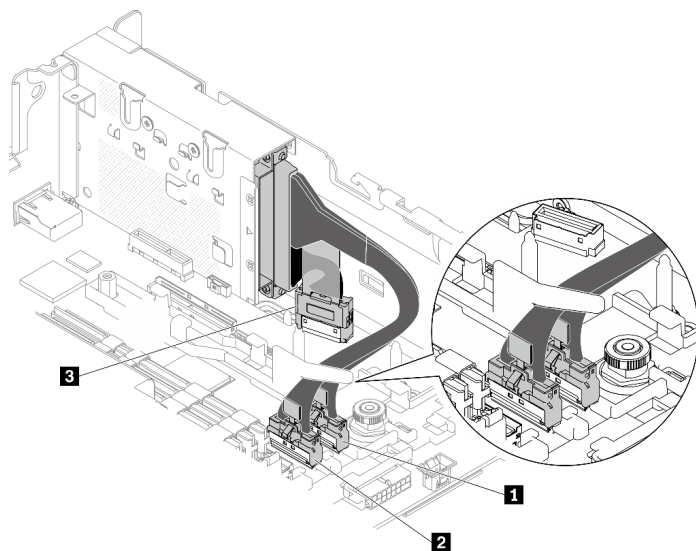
Disposición de los cables para el adaptador OCP 3.0 Ethernet
